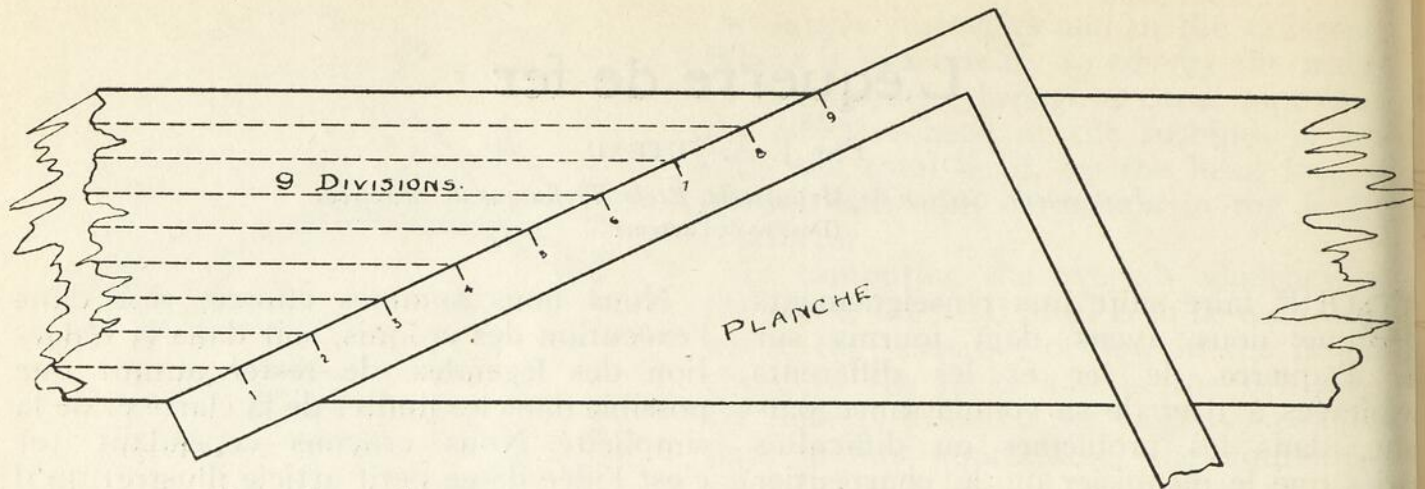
FIG. B.— COMMENT DIVISER LA LARGEUR D'UNE PLANCHE.
